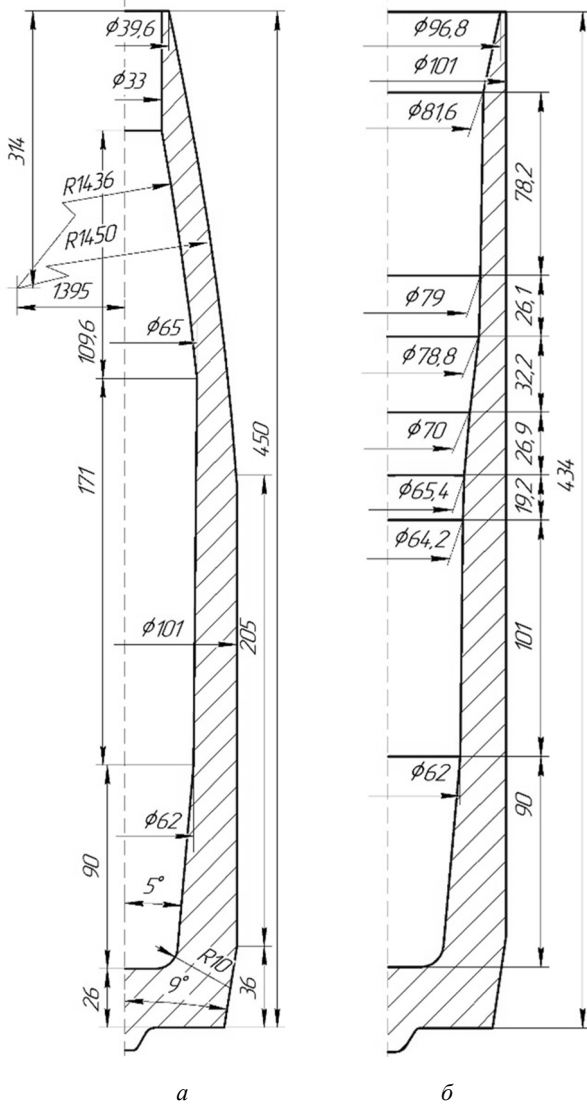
Ескізи половини виробу і половини вихідної заготовки з розмірами: а – половина виробу, б – половина заготовки
